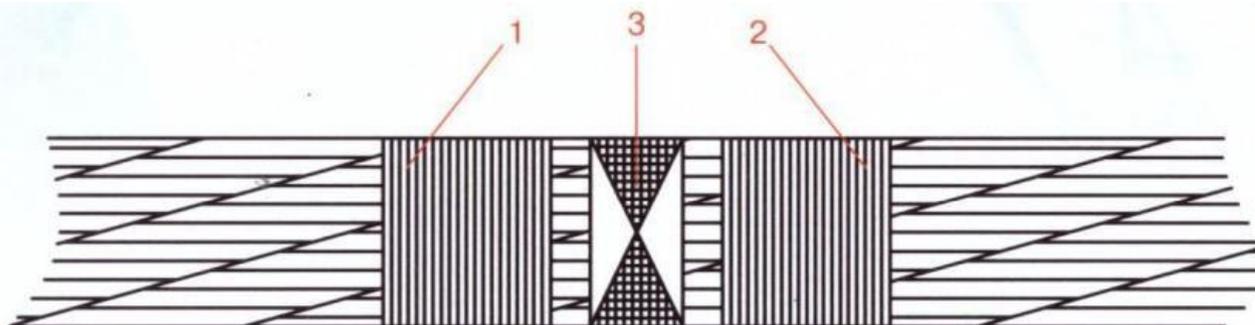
Сварное соединение старого и нового каната
